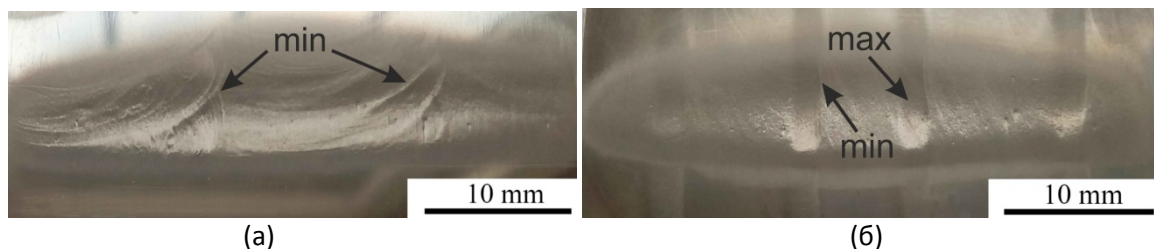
Рельеф поверхности наплавки после абразивного изнашивания
